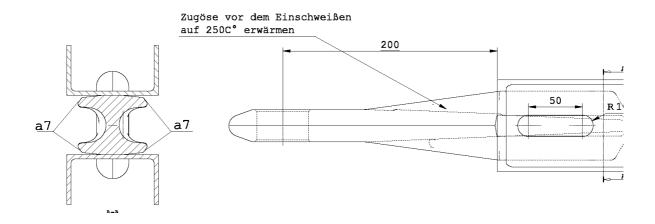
Exemplarischer Schweißnahtanschluss
